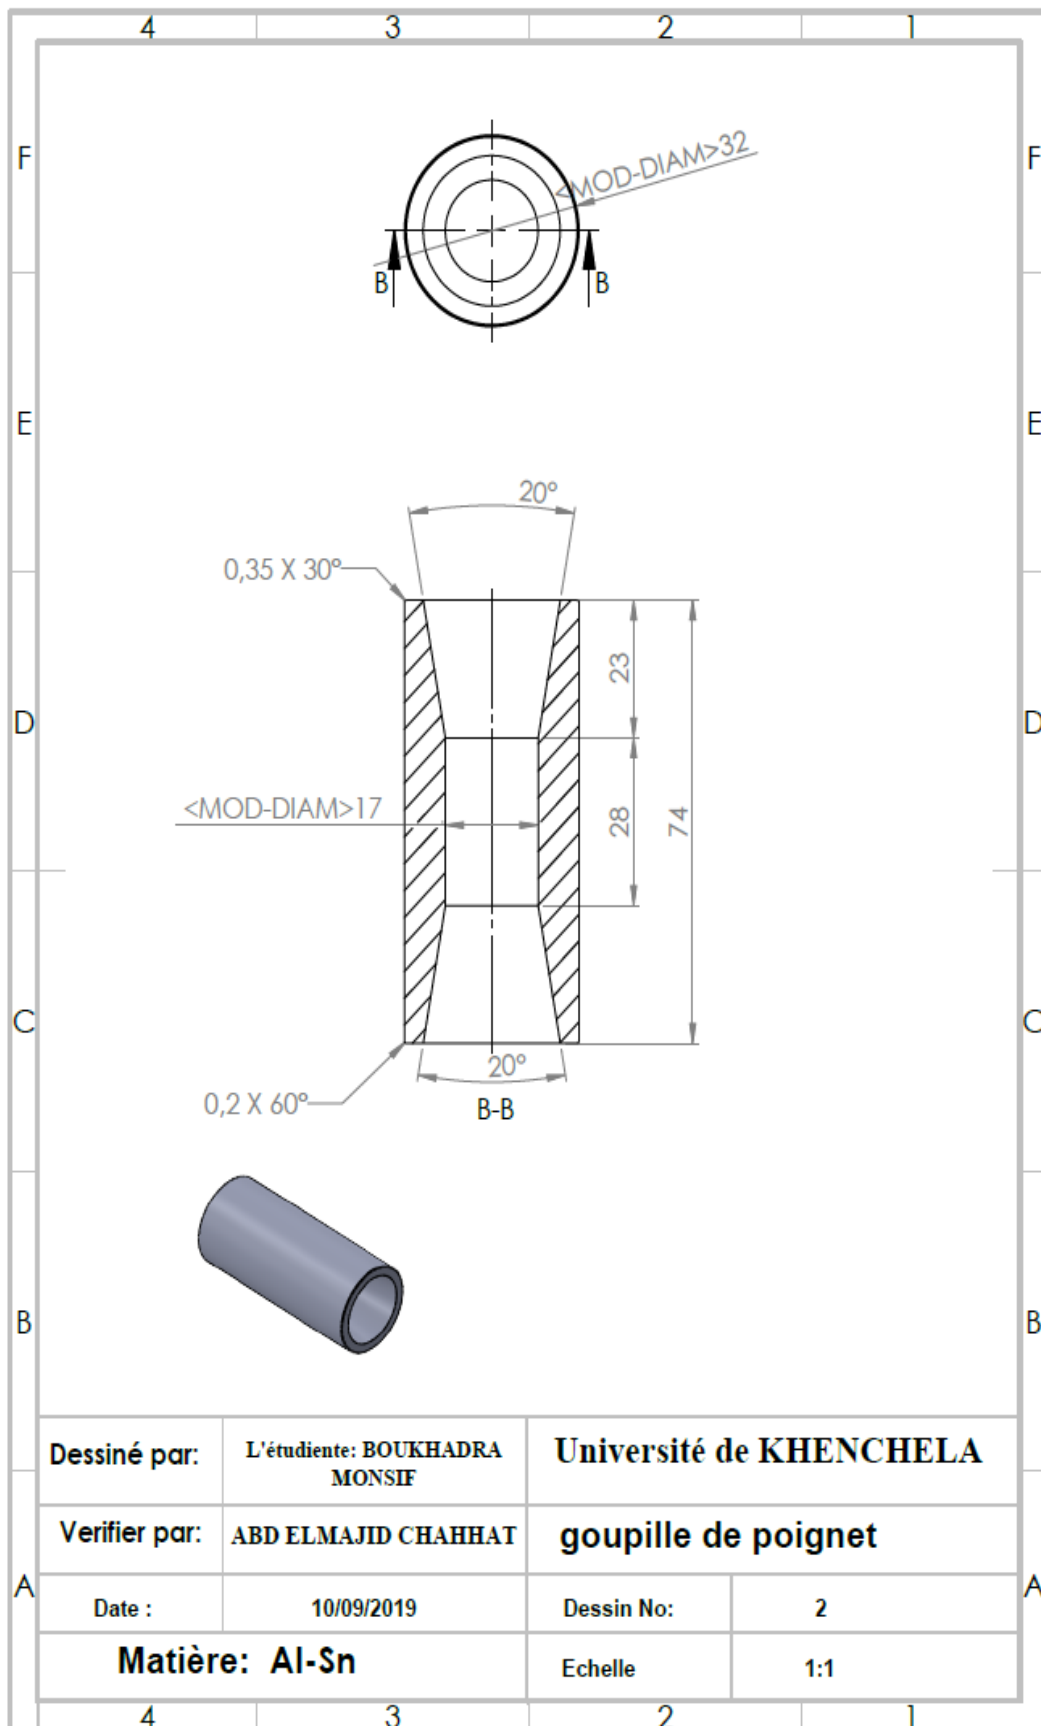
Dessin technique d'un l'axe piston en solidworks
